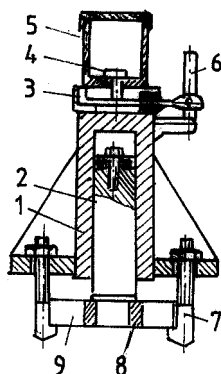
Extractor hidraulic*: 1-cilindru; 2-piston; 3-pompă cu plunjer (plunjer); 4-dop perforat; 5-rezervor cu ulei; 6-mâner; 7-clește; 8-bucșă; 9-piesă
